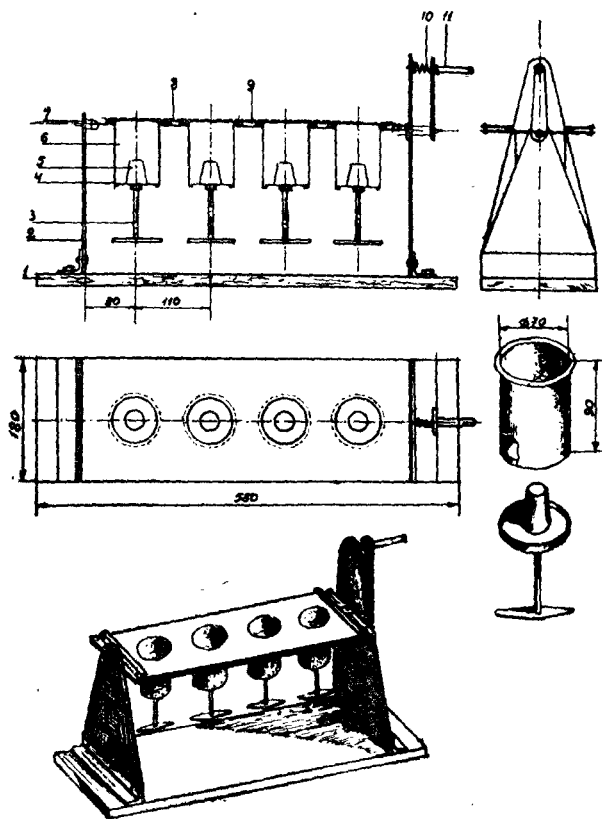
Станок для изготовления торфоперегнойных горшочков. 1 — станция; 2 — боковина; 3 — ручка пуансона; 4 — диск; 5 — пуансон; 6 — стакан; 7 — хвостовик плиты; 8 — верхняя поворотная плита; 9 — нижняя поворотная плита; 10 — пружина; 11 — поворот с конусным фиксатором.
